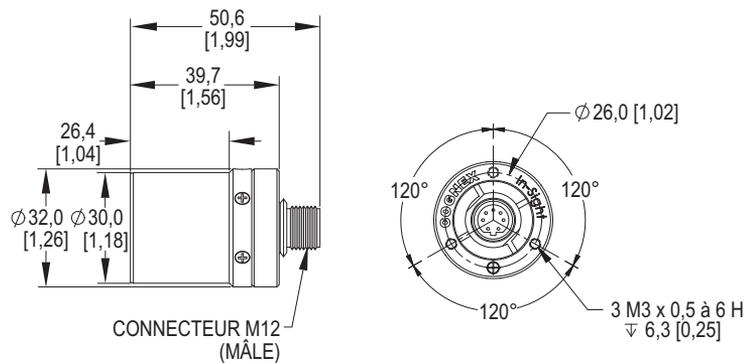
Dimensions du capteur de vision In-Sight 5400R
